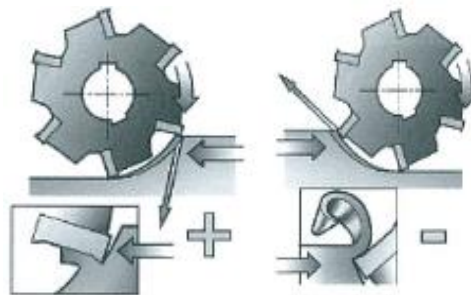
Fresagem concordante (esquerda) e fresagem discordante (direita).
